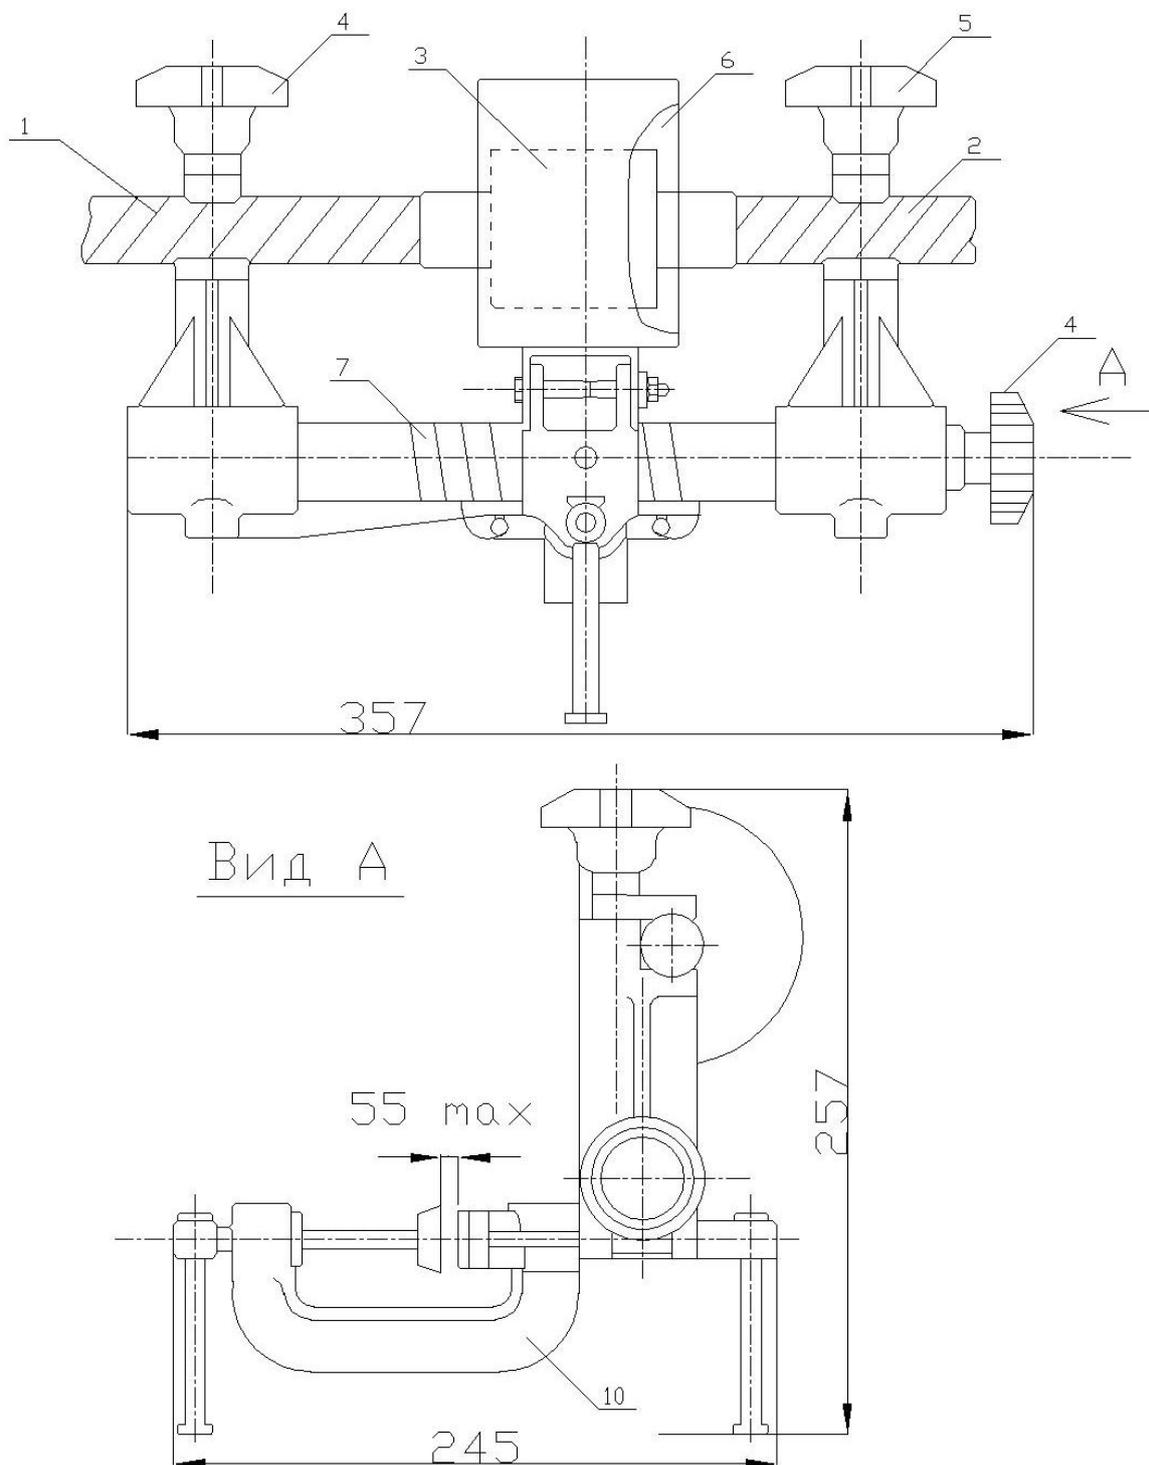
Сварочное приспособление для термитной сварки проводов сечением до  $240 \text{ мм}^2$ :
